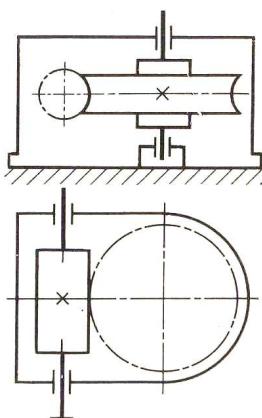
Червячный редуктор с боковым расположением червяка
